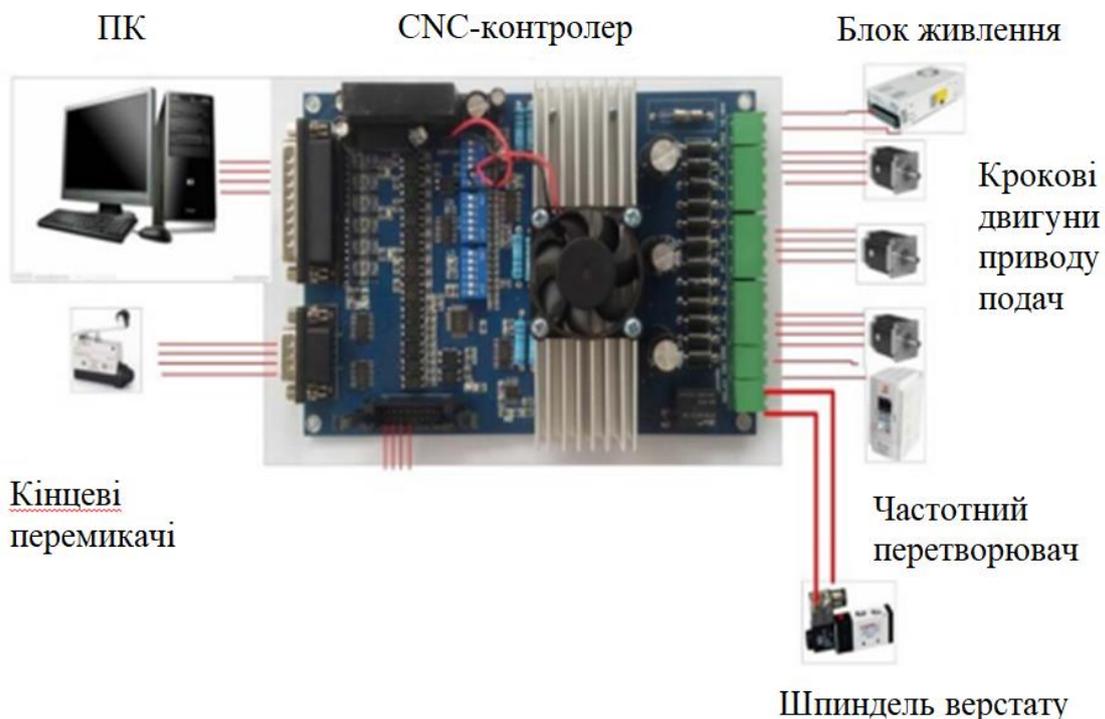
Система керування верстата на базі CNC-контролера та ПК
